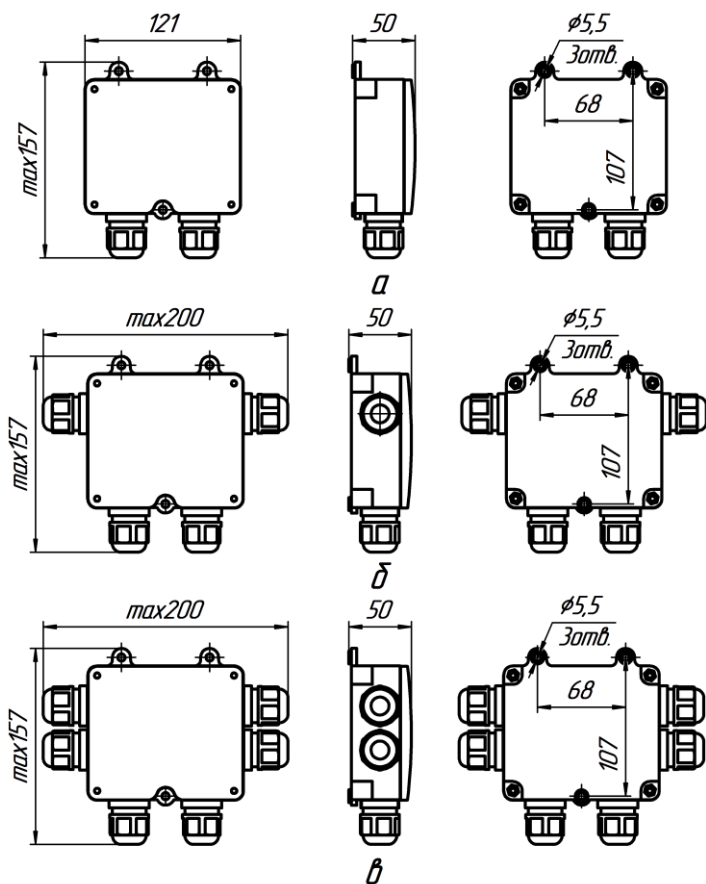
Установочные и габаритные размеры коробки соединительной.
